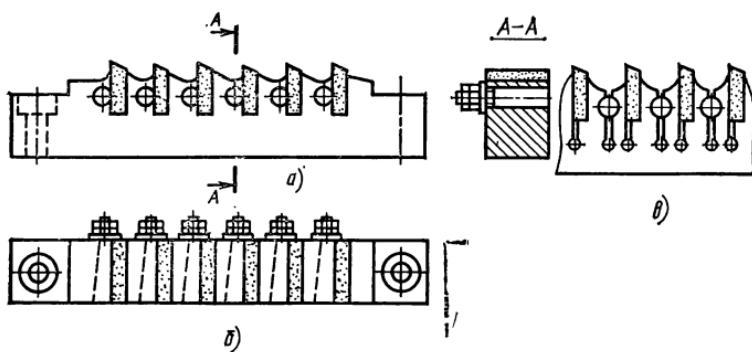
Сборные твердосплавные протяжки с креплением зубьев-пластин коническим штифтом
